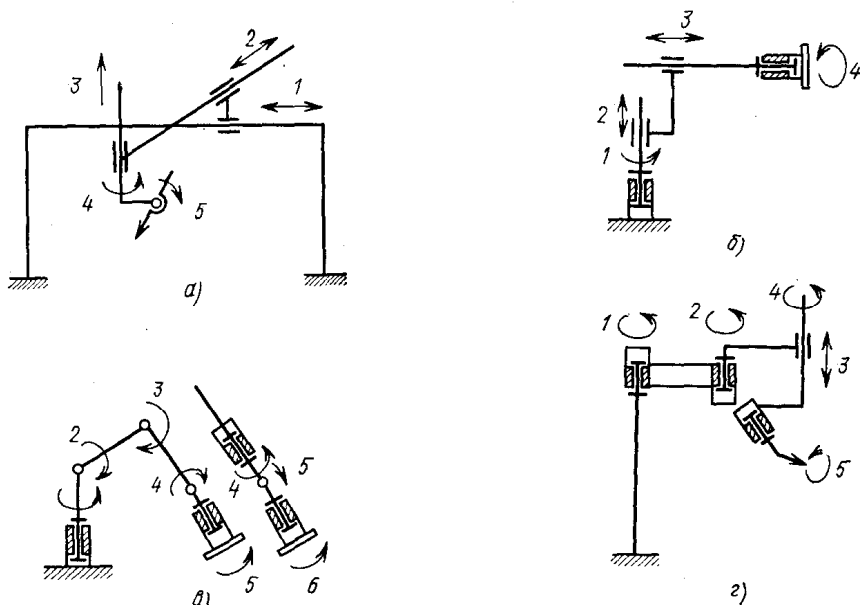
Кинематические схемы ПР, используемых в сварочном производстве:
